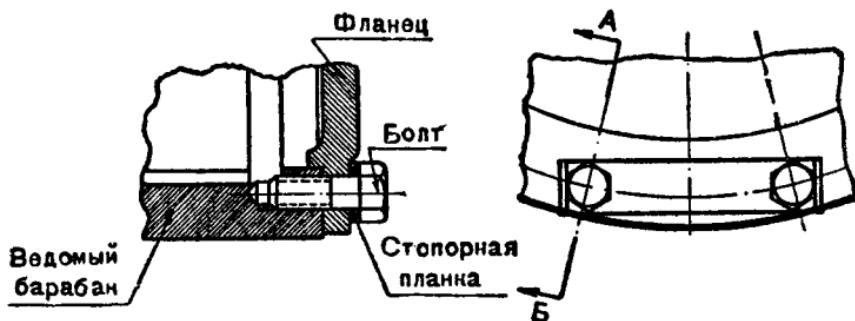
Стопорная планка под болты крепления фланца к барабану и схема её установки.
